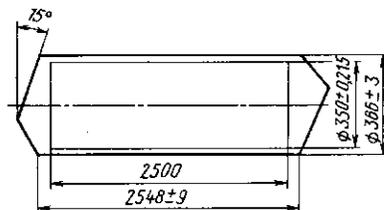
Рабочий чертеж вала, изготовляемого ковкой на прессе
